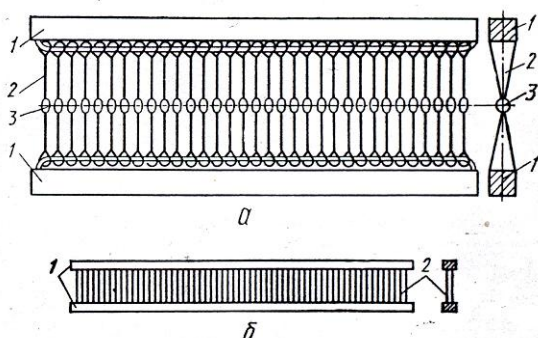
Детали ткацкого станка: а – ремизка; б – бердо
